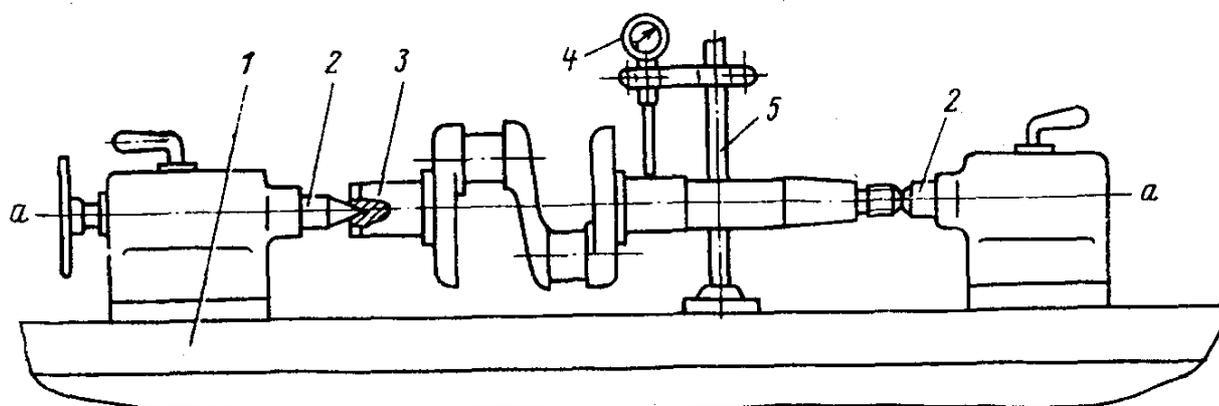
Приспособление для контроля изгиба коленчатого вала компрессора
